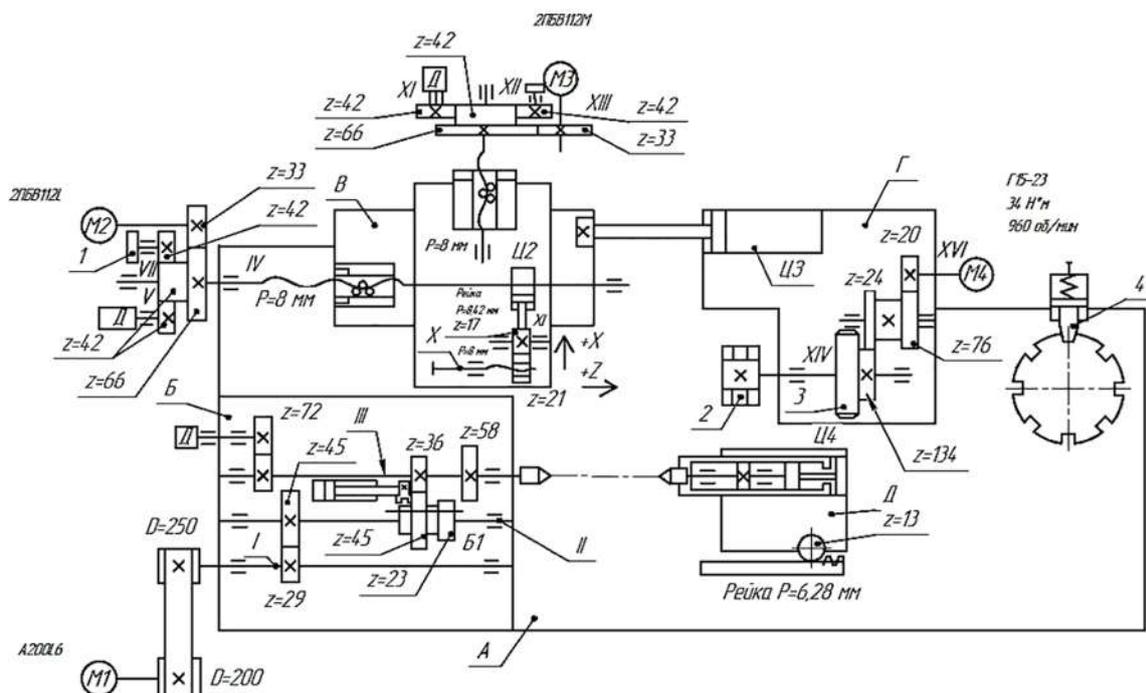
Кинематическая схема станка с ЧПУ 1725МФ3
